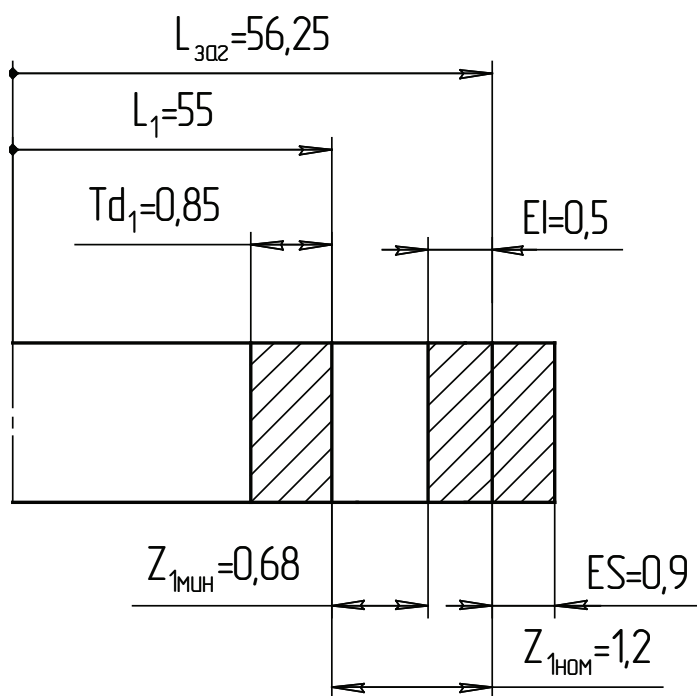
Размерная схема обработки 2-й поверхности (наружная)
